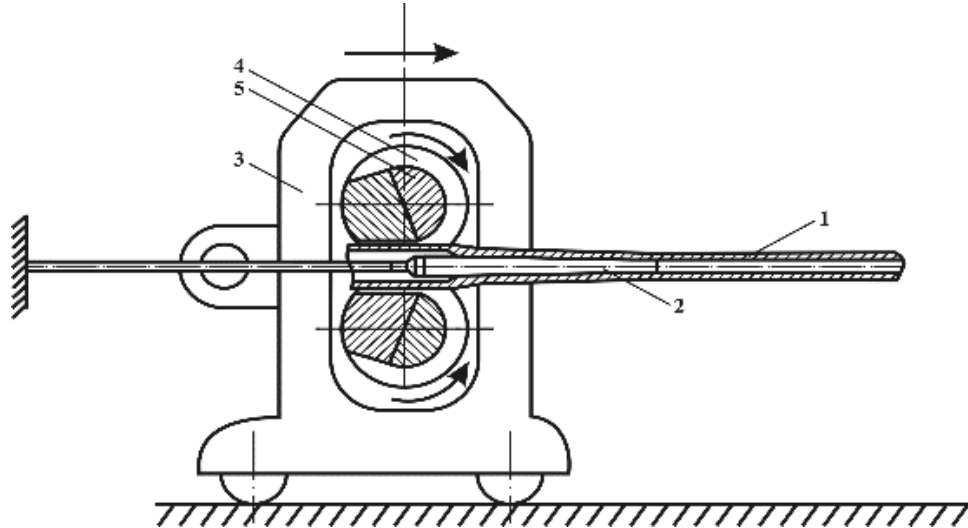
Кліть стану ХПТ, труба та оправка зі стрижнем: 1 – прокатана труба ; 2 – оправка та робочий конус деформування на ній; 3 – станина; 4 – валок; 5 – калібр
